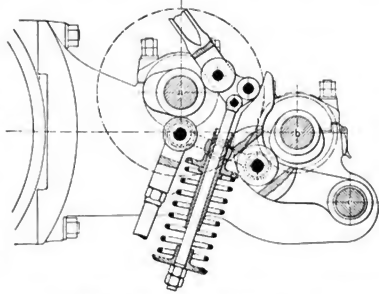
Steuerungsantrieb der Dingerschen Maschinenfabrik, Aktiengesellschaft in Zweibrücken.
